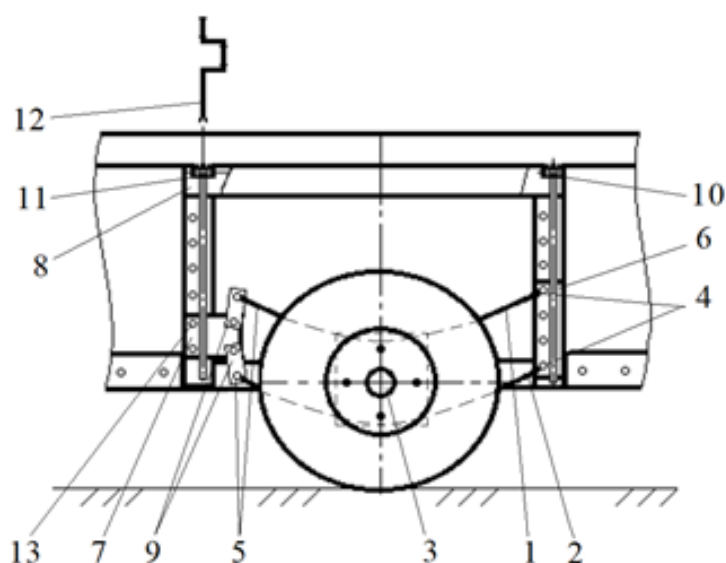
Схема узла подвески: 1, 2 – рессоры; 3 – консольная ось колеса; 4, 5 – передние и задние концы рессор; 6, 7 – кронштейны; 8 – рама; 9 – серёга; 10, 11 – винтовой механизм; 12 – ключ; 13 – фиксатор
